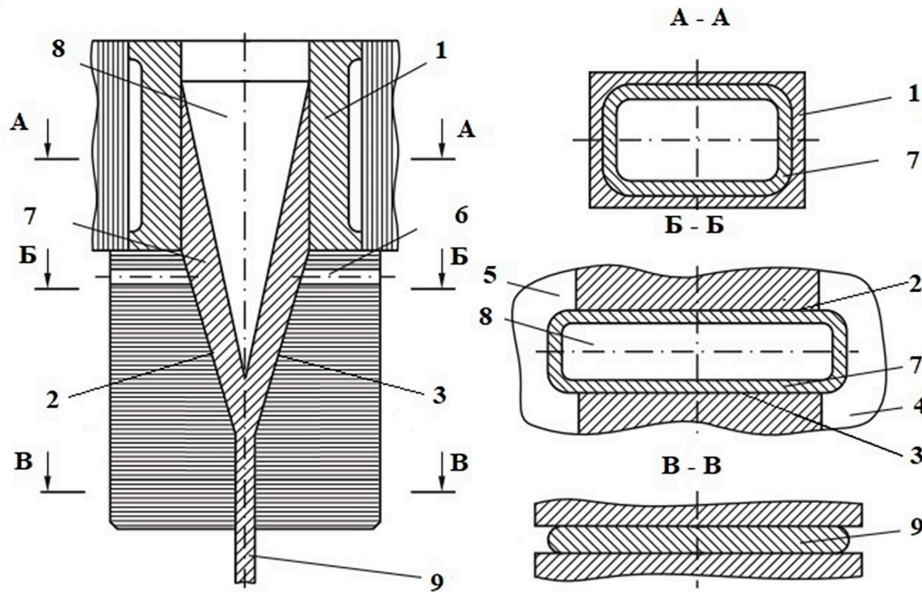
Схема комплекта агрегатов МНЛДЗ в сборе:
